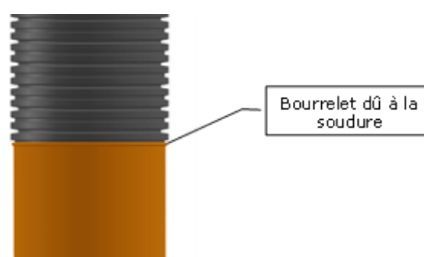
Détail du soudage entre un tuyau flexible et un tuyau rigide
